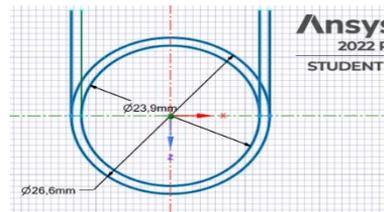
pipa sudut 60° (Tampak Depan)
